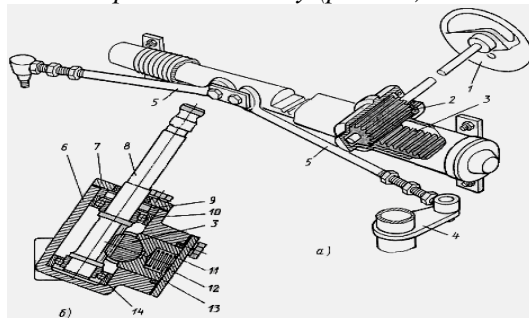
Рейковий рульовий механізм (1- рульове колесо; 2- шестерня рульового валу; 3- рейка; 4- поворотний важіль; 5-поперечні тяги; 6- корпус рульового механізму; 7- кришка; 8- вал шестерні; 9- сальник; 10, 14 – підшипник; 11- кришка рейки; 12- пружина підтискна рейки; 13- втулка рейки).
